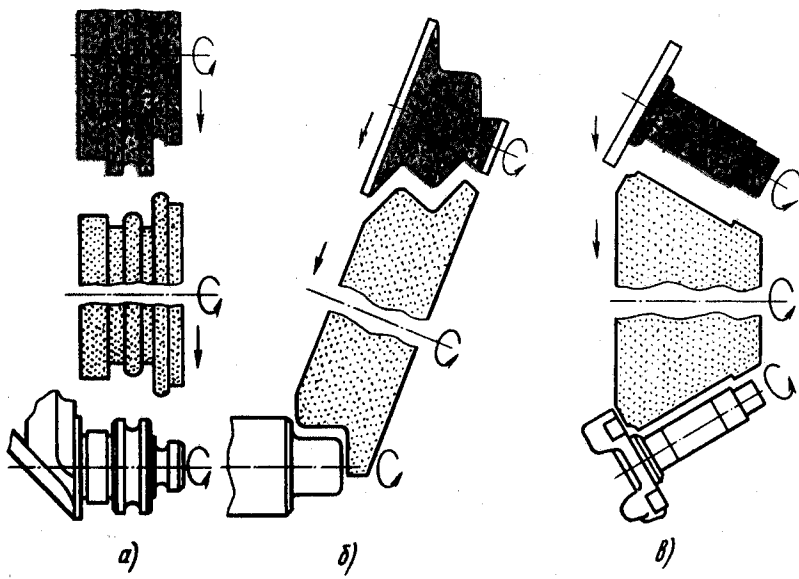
Схема совмещенной правки рабочей поверхности круга алмазными роликами и шлифования:
